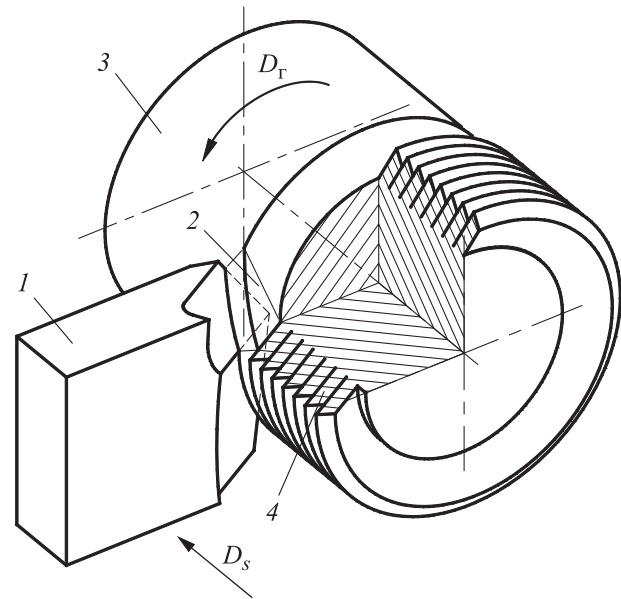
Схема формирования упрочненного макрорельефа методом ДР:
